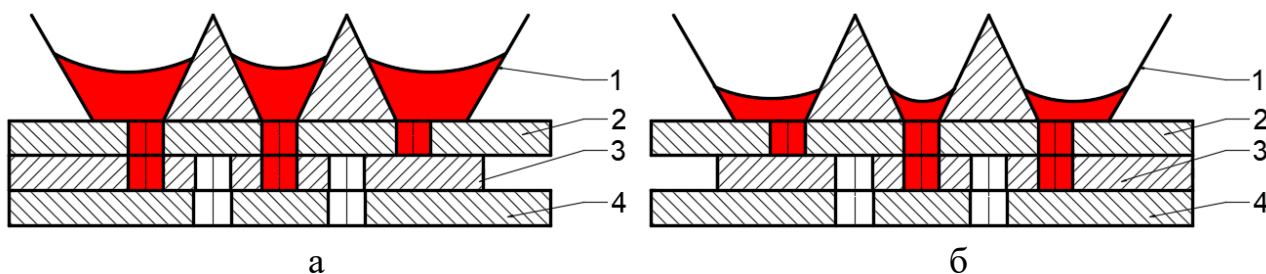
Конфигурация шиберного дозатора в процессе дозирования: а) шибер смещен влево; б) шибер смещен вправо: 1 – нижний корпус; 2 – шибер; 3 – верхний корпус; 4 – шток цилиндра
